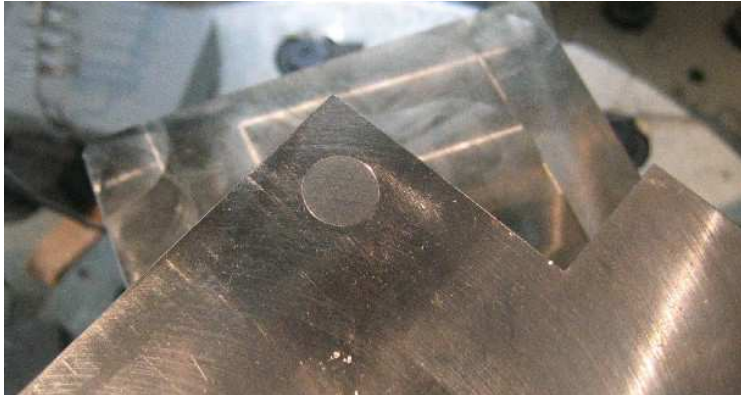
Detalhe da face do bloco AB3 com o sensor acoplado
